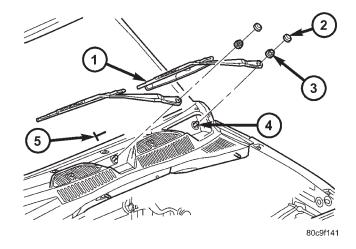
Desmontaje e instalación de brazo de limpiador delantero
